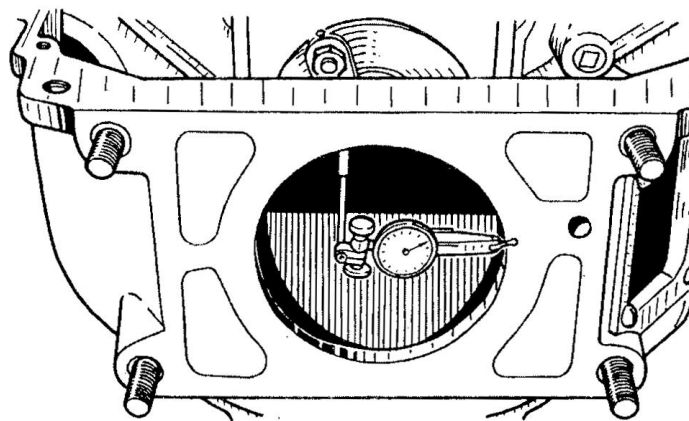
Проверка перпендикулярности заднего торца картера сцепления к оси коленчатого вала
